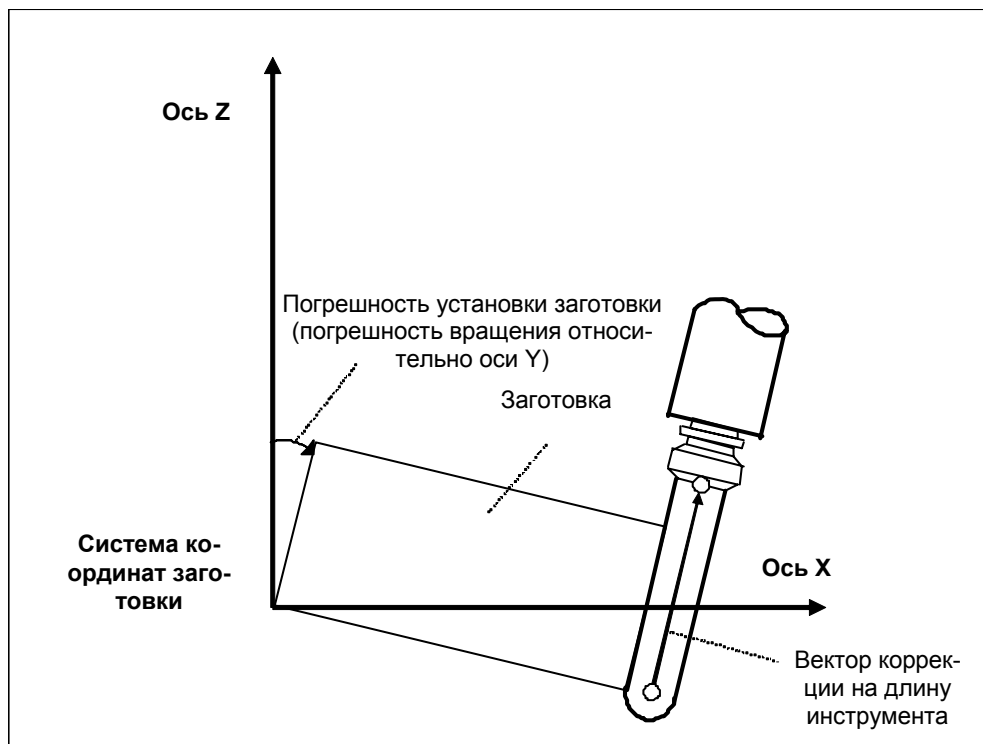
(r) Заготовка обрабатывается боковой стороной инструмента при наличии погрешности на установку заготовки (Если RCM=1)
